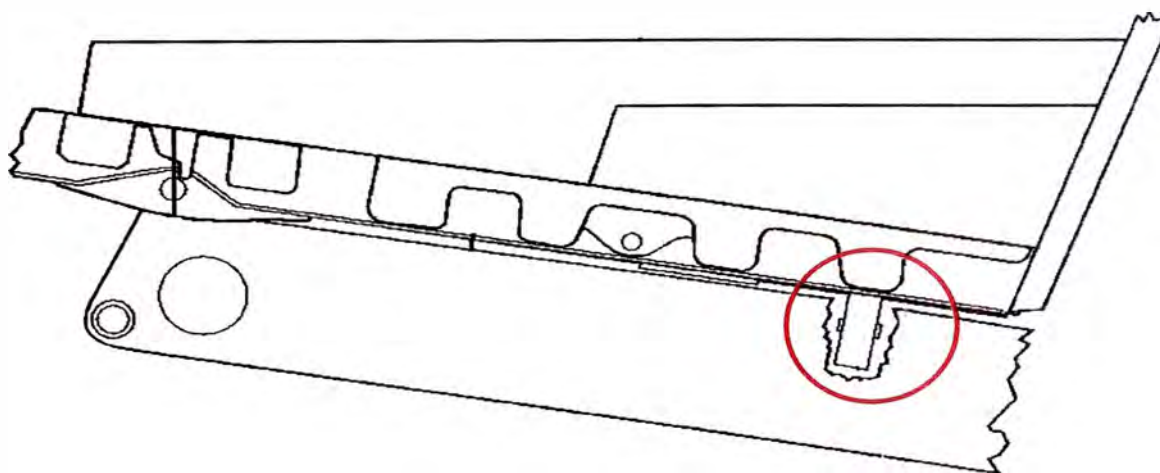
Fisura en trunion de cilindro de levante derecho.
